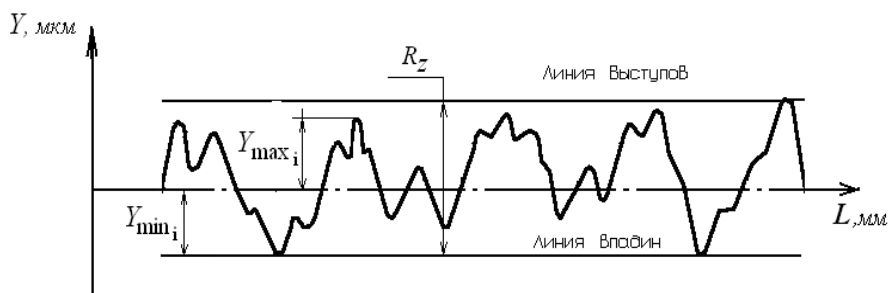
Реальный (фактический) профиль шероховатости, формируемый при движении лезвия инструмента вдоль траектории его движения (винтовой линии) на пути резания L
